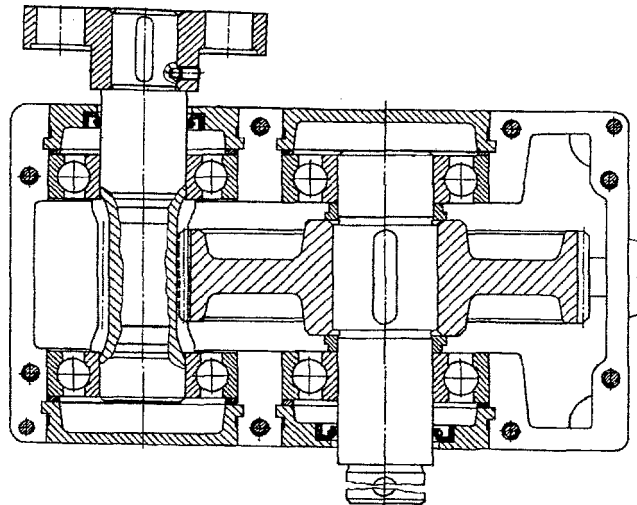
Цилиндрический горизонтальный одноступенчатый редуктор.
